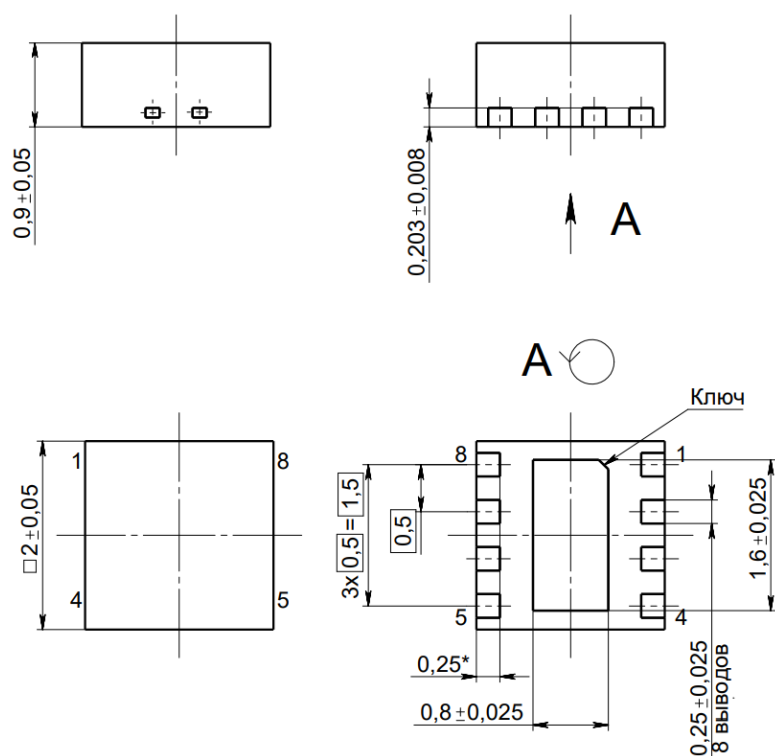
Габаритный чертеж корпуса 5239.8-1 К (размеры в мм)
